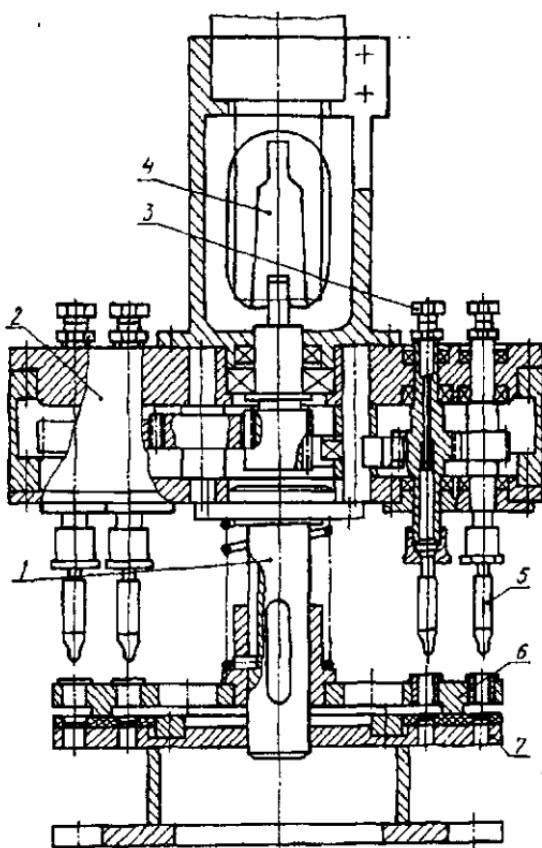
Приспособление для сверления отверстий в накладке ведомого диска сцепления:
